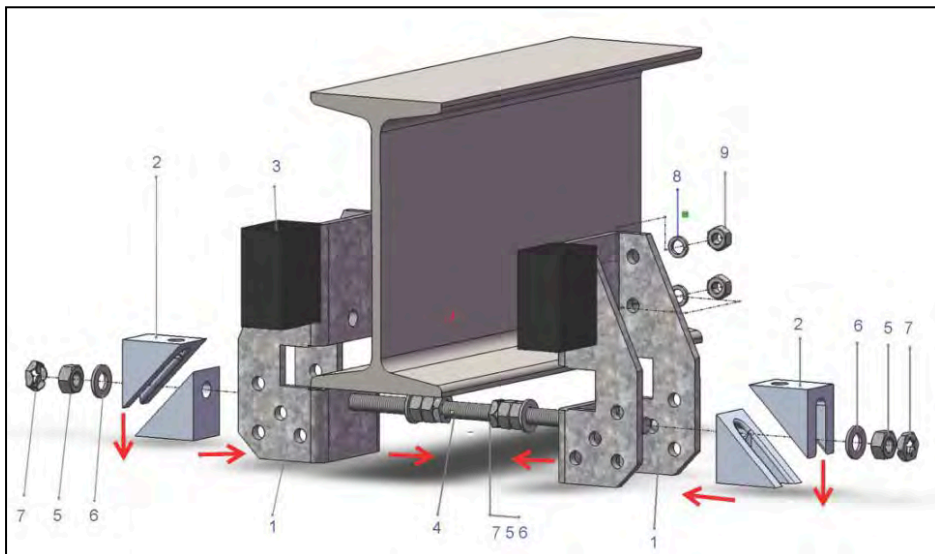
Alternativ 1 för montering på balkens undre fläns. (vanligast)
